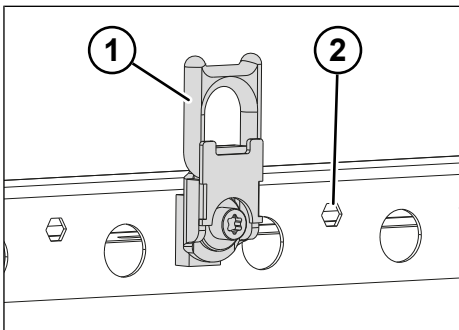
Multi Lash la cadrul exterior Multi Lock
